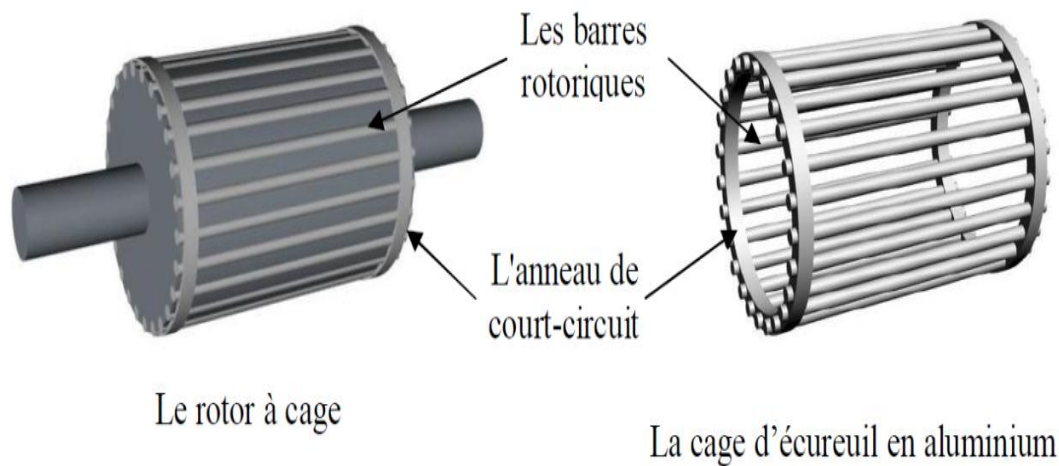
Photo du rotor d'une machine asynchrone [6].
